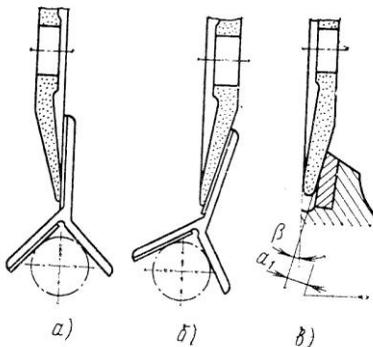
Схема установки шлифовального круга при заточке передней поверхности:
